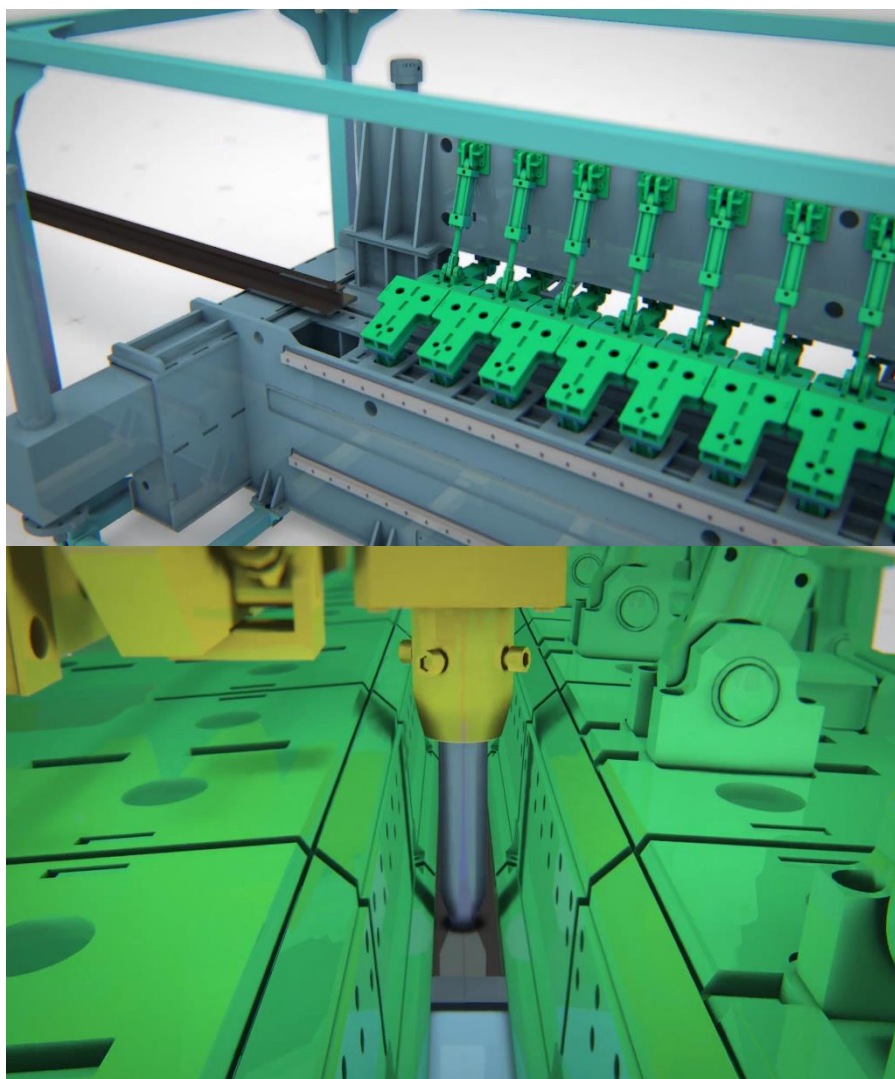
Сварка перемешиванием двутавров (рельсов).
